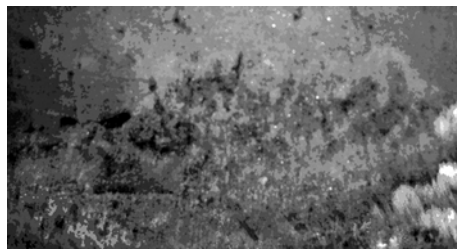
Дефект поверхности отливки "раковины, заполненные углеродом"
